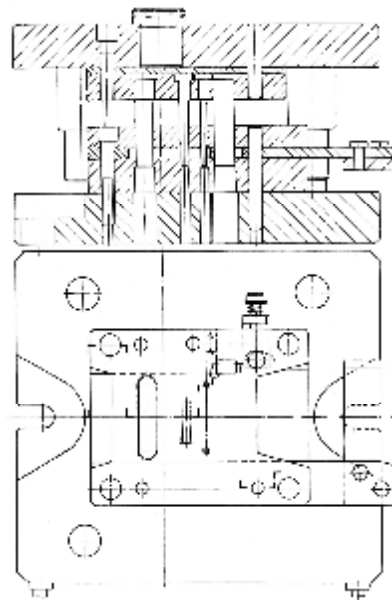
Штамп для виготовлення деталей на ОАО «Кредмаш»
